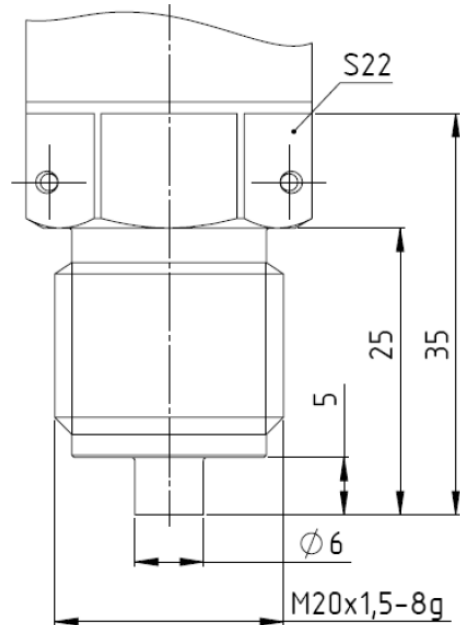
Присоединительный штуцер тип 2 по ГОСТ 2405-88, черт. 21
